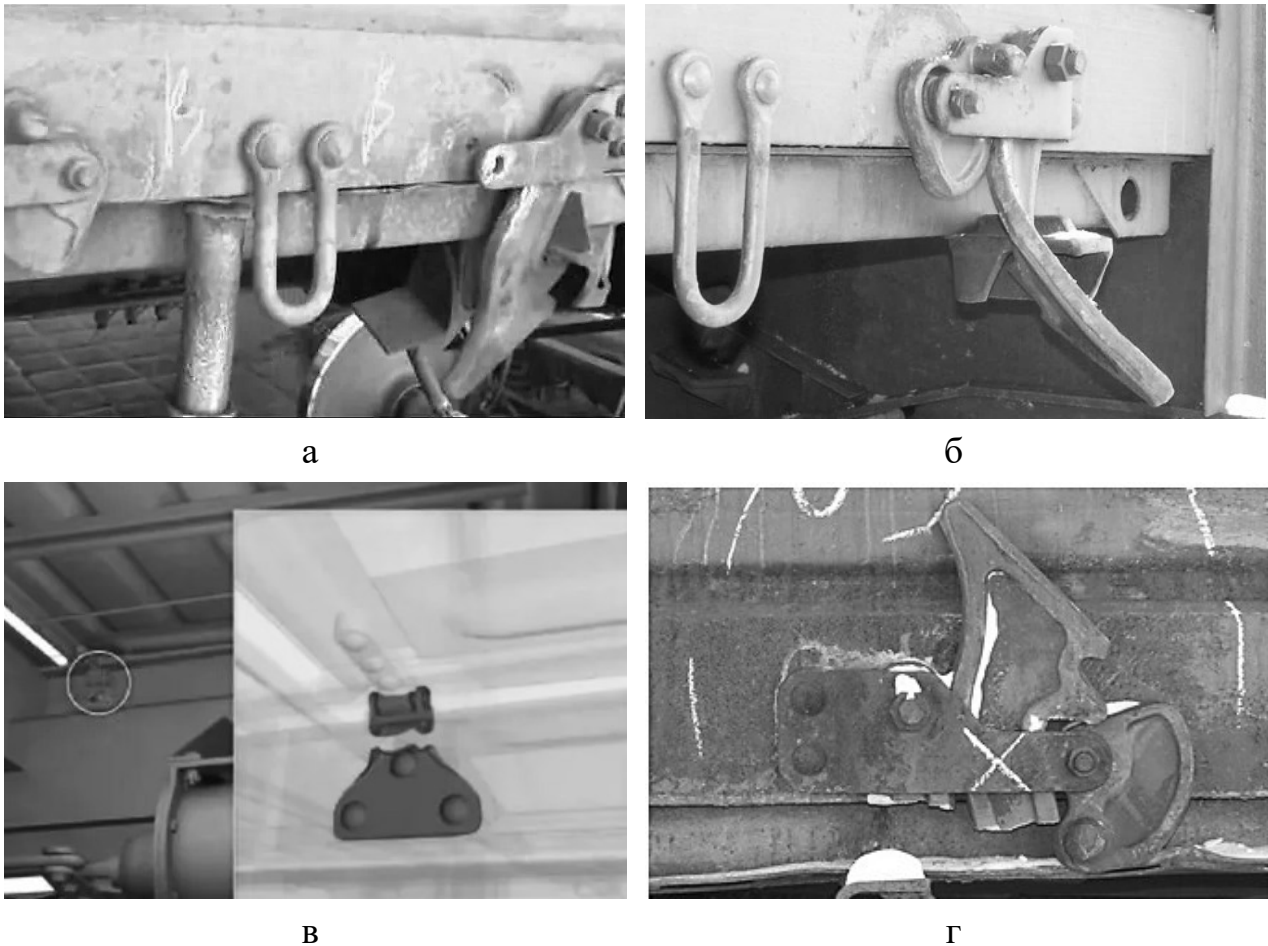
Дефекты и повреждения деталей механизма закрывания крышки люка полувагона:
